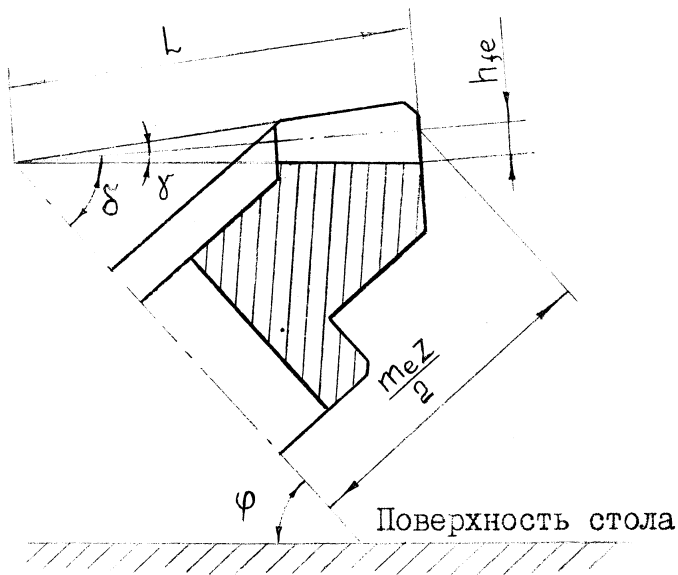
Схема установки заготовки конического колеса при фрезеровании впадин зуба
